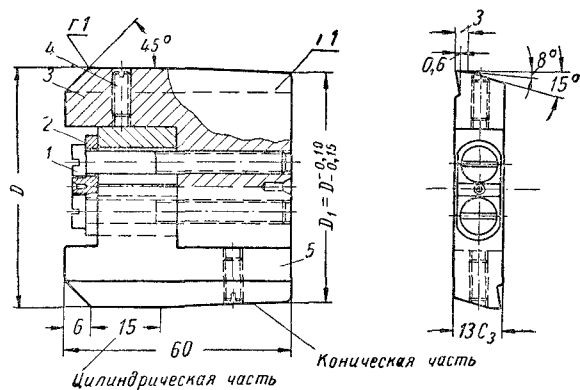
Борштанга для расточки цилиндра протяжного станка.
